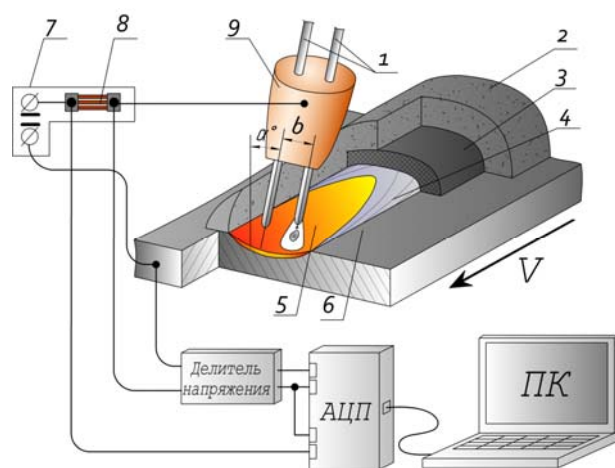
Схема наплавки расщепленным электродом с регистрацией сварочного тока и напряжения на дуге: 1 – электродные проволоки; 2 – сварочный флюс; 3 – шлаковая корка; 4 – наплавленный металл; 5 – сварочная ванна; 6 – изделие; 7 – источник сварочного тока LAF 1000; 8 – измерительный шунт; 9 – токоподводящий узел; b – межэлектродное расстояние; α – угол наклона электрода от вертикальной плоскости; АЦП – аналого-цифровой преобразователь
